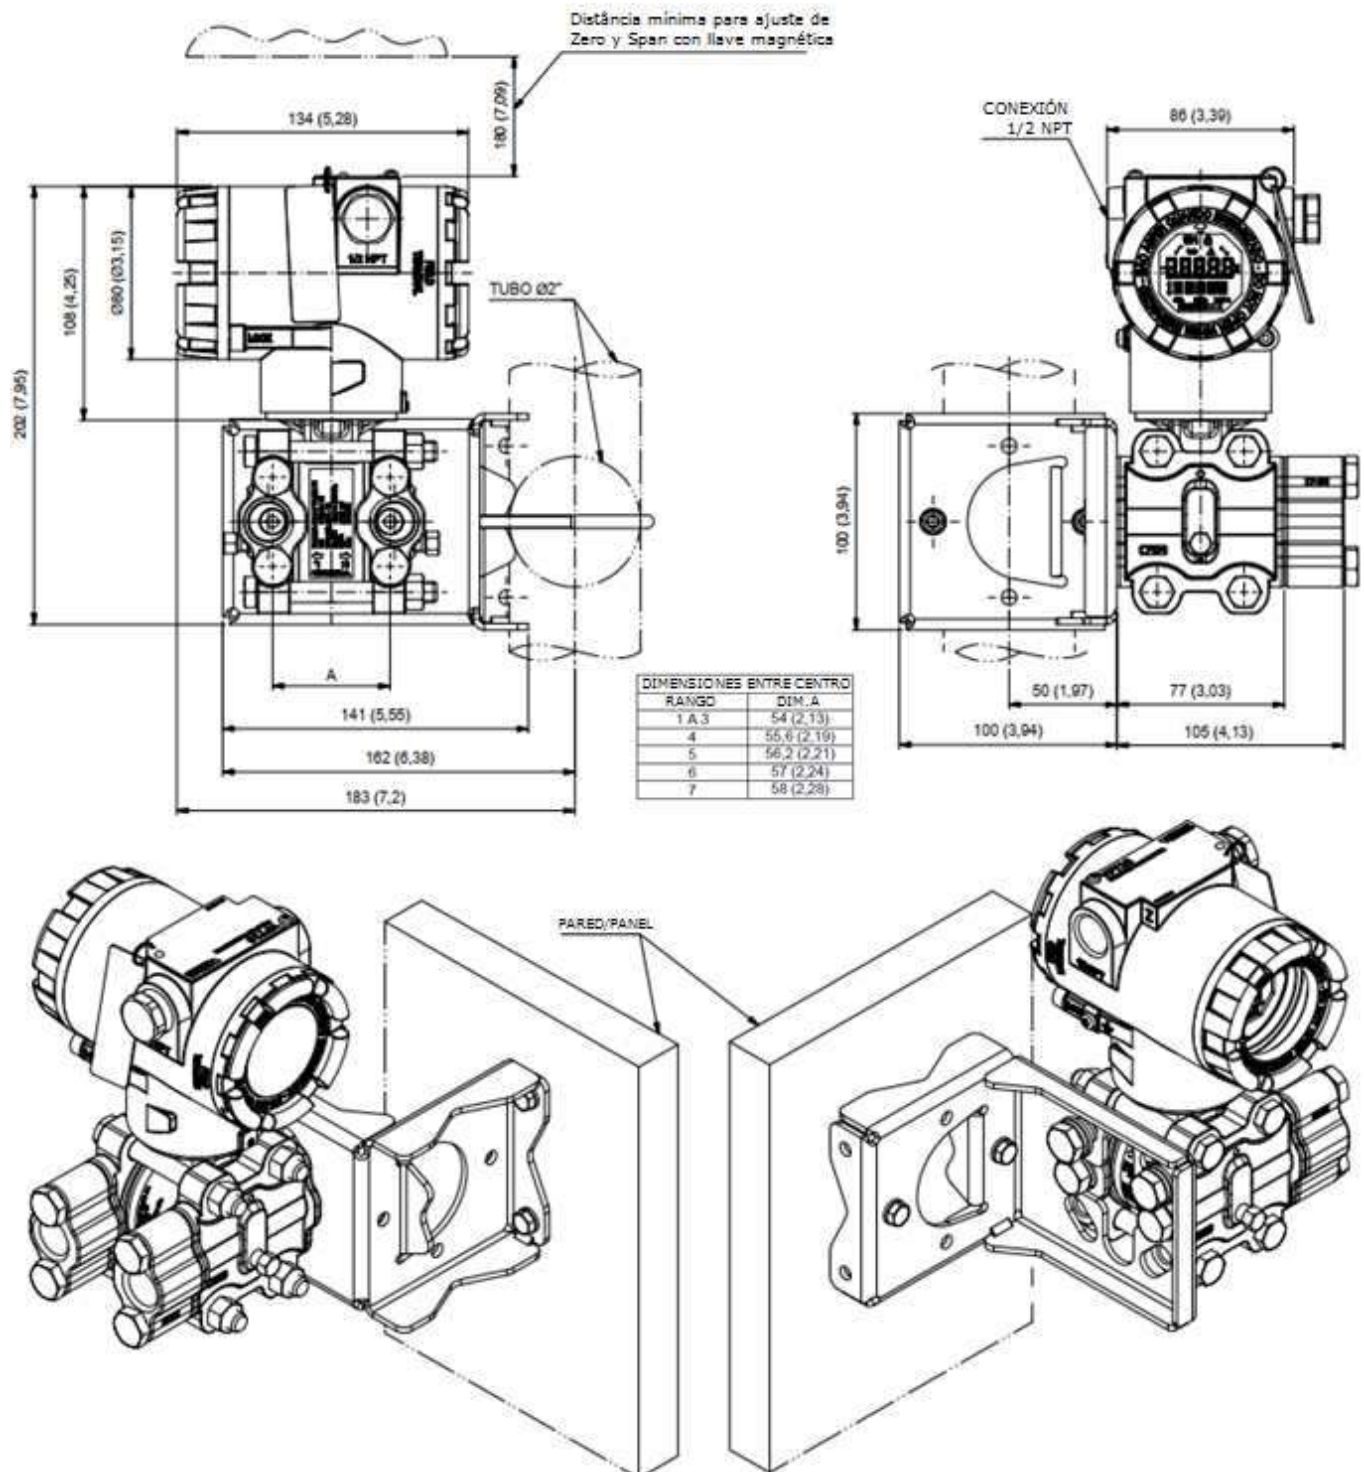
Diseño dimensional y esquema de montaje del VPT10-H.
